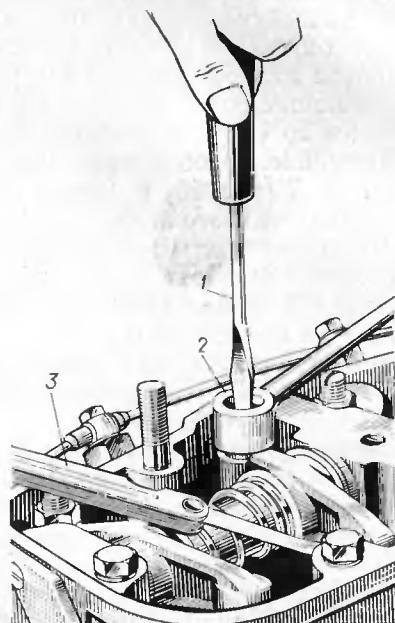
Регулировка зазора между коромыслом и штоком клапана:
